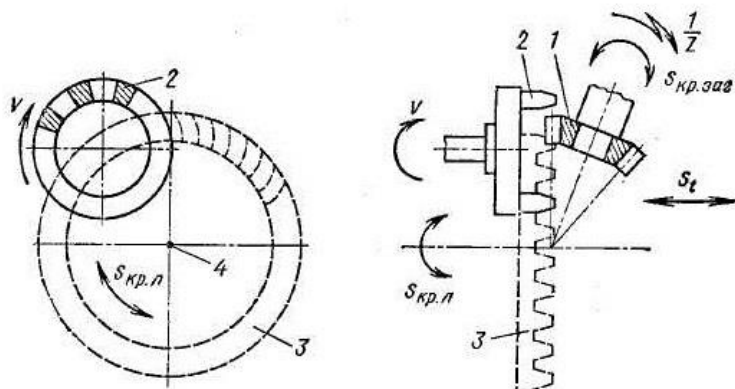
Схема нарезания конического колеса с арочными зубьями
